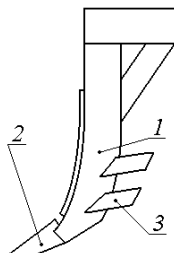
Конструктивна схема чизеля - розпушувача RZ-220.7:
